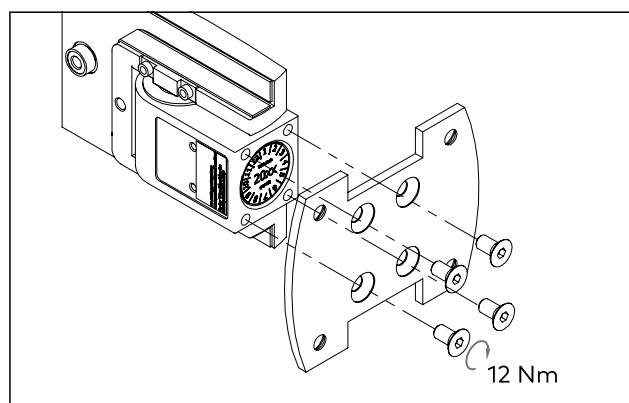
Fixation des plaques de montage à la paumelle à rappel
